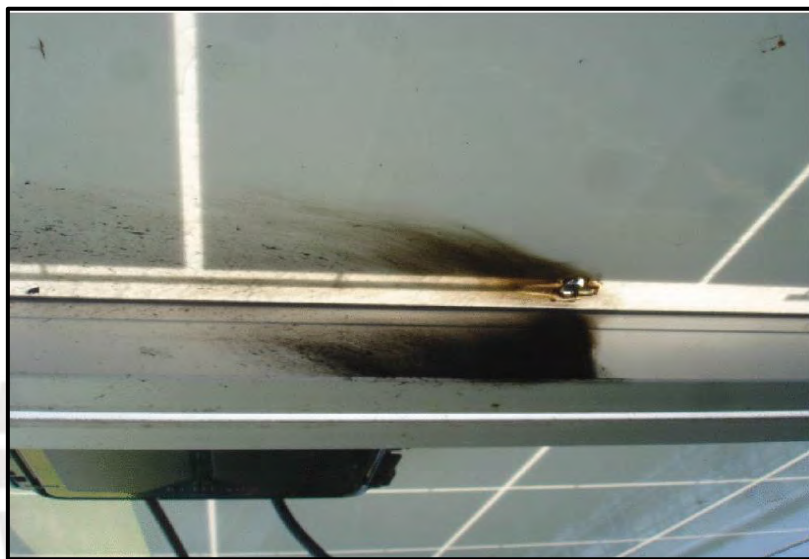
Ejemplo de punto de soldadura quemado [37], [60]
